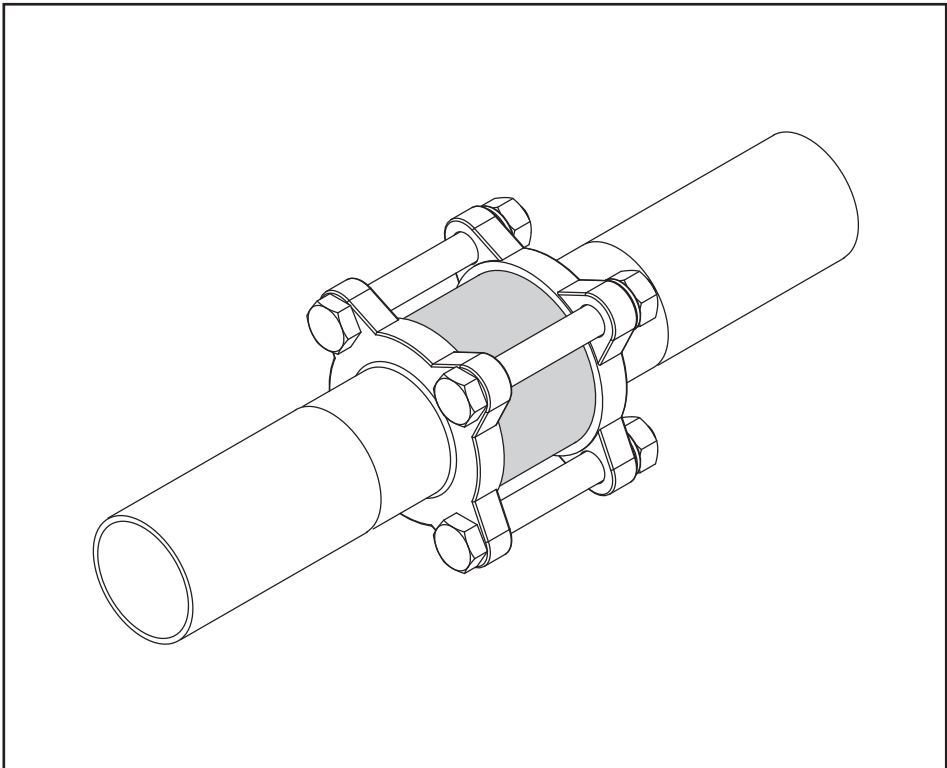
Kugelhähne, Montage Anschweißenden, Anschweißen der Anschlüssen (Abbildung zeigt Art. ZE311064)
